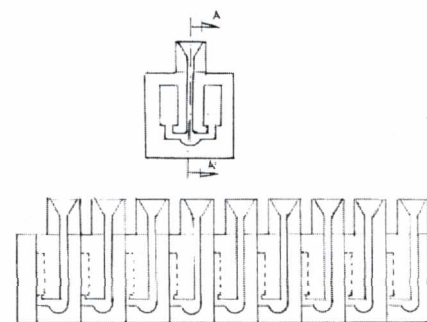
esquema del colado en fuente de las placas para cupones de soldadura
